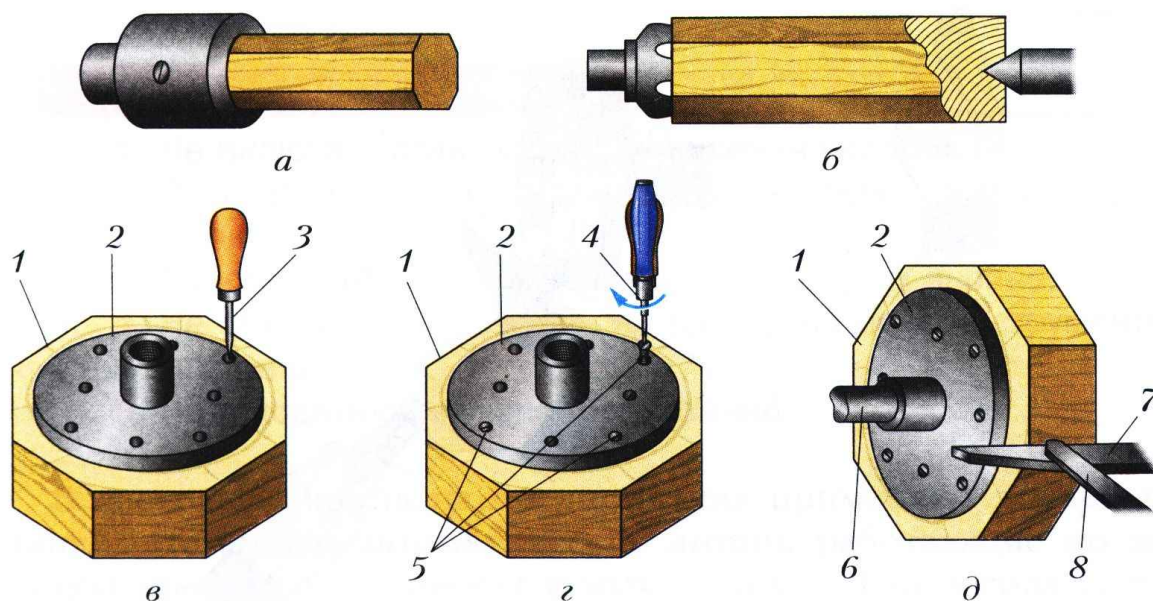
Крепление заготовки: *а* – в патроне винтом; *б* – с помощью трезубца и заднего центра; *в, г, д* – на планшайбе: 1 – заготовка; 2 – планшайба; 3 – шило; 4 – отвёртка; 5 – шурупы; 6 – шпиндель; 7 – подручник; 8 – режущий инструмент (стамеска)
